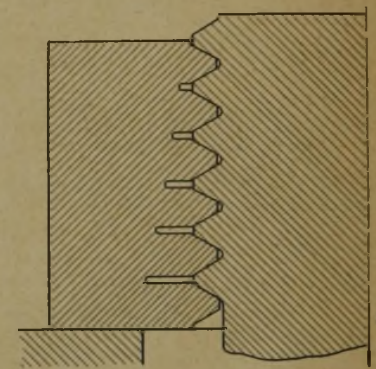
Gewinde nach J. R. Solt für gleichmäßige Belastung der Gänge auch bei der üblichen Mutterform.
